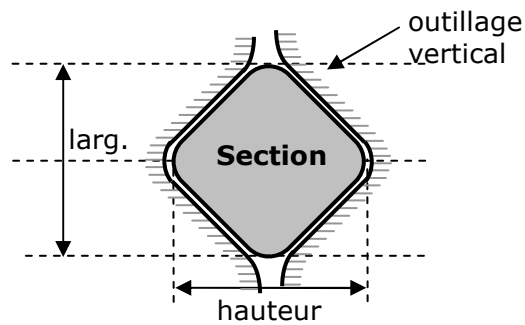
Section de la barre APRES la passe de laminage pour le cas de cylindres verticaux
